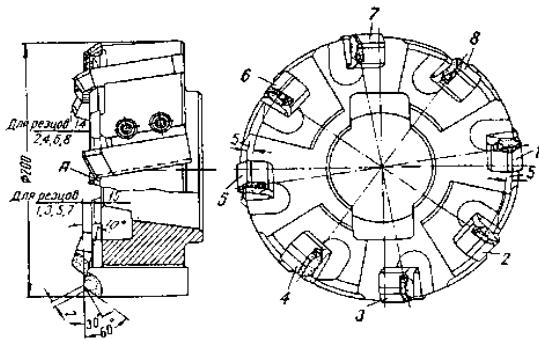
Торцева фреза двохступінчаста насадна із вставними різцями 1,3,5,7 – різці першої ступені; 2,4,6,8 – різці другої ступені
